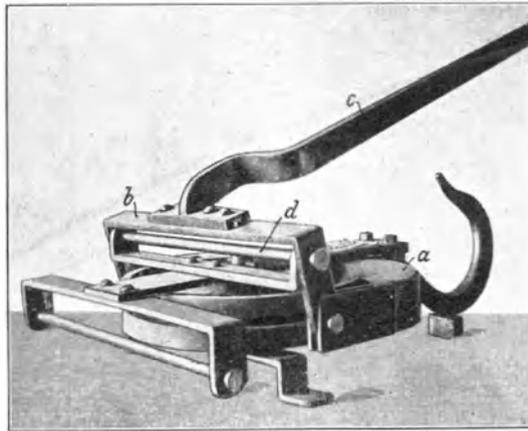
Scheibenbremse der Köln-Ehrenfelder Maschinenbauanstalt.
